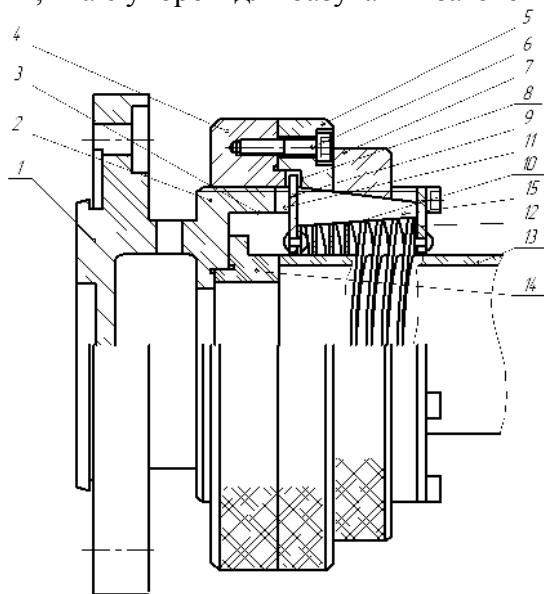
Конструкція цангово-гвинтового затискного патрона
